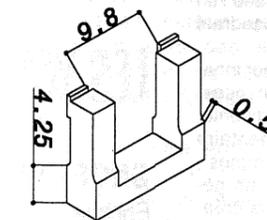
Retirer la pièce de la machine, scier et retirer la partie centrale. remonter sur la fraiseuse et terminer à la fraise de 8. Replacer horizontalement et lamer toute la surface à 0.5 mm. Faire un congé de 2.
